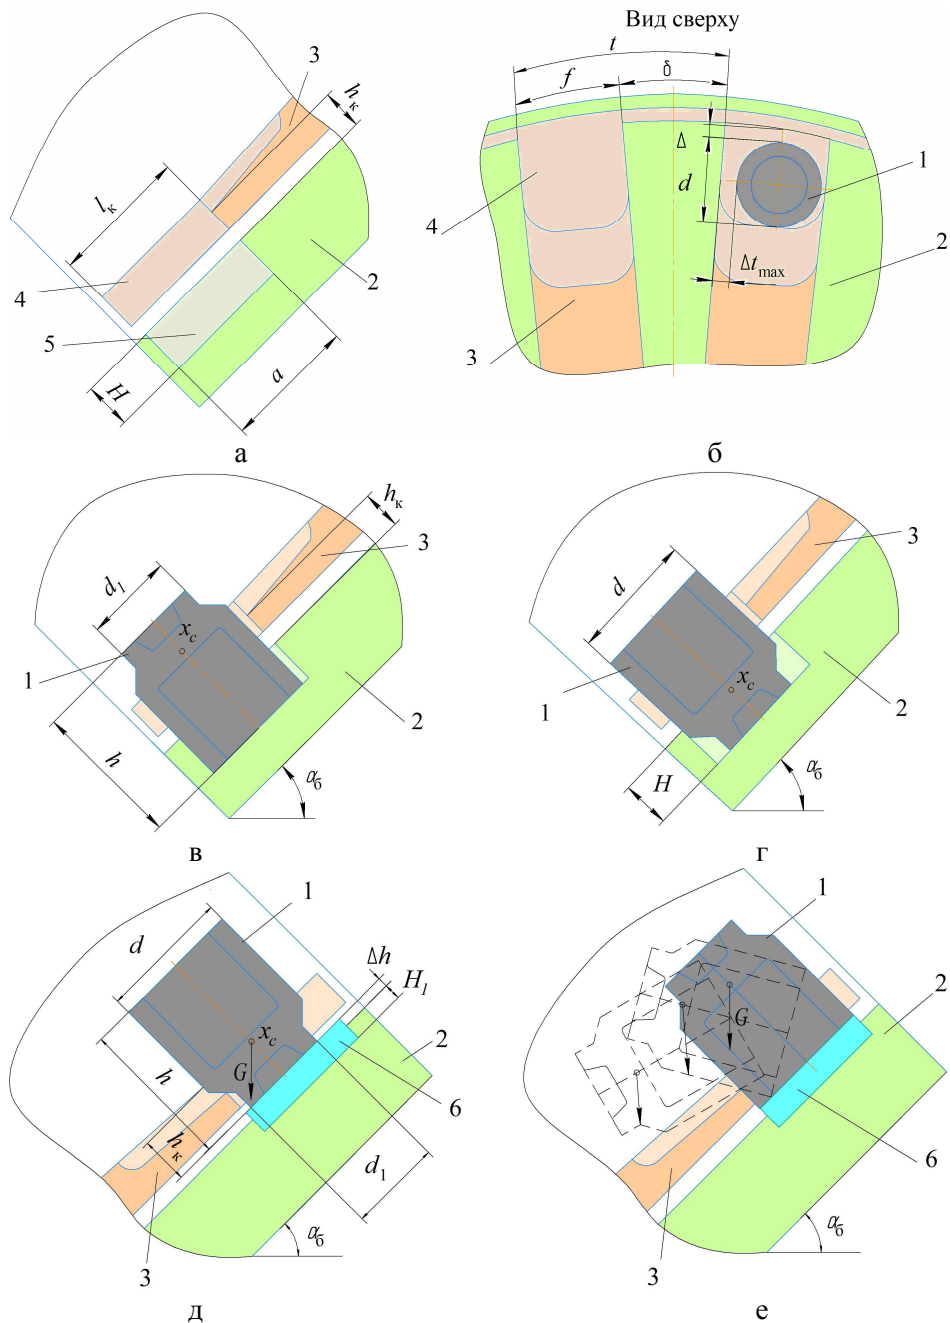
Схемы совершенствованного бункерного загрузочного устройства для деталей, близких к равноразмерным с асимметрией по торцам: а – общий вид; б – вид сверху; в, г – в нижней части бункера БЗУ с запавшей в разных положениях деталью; д, е – в верхней части бункера БЗУ с запавшей деталью: 1 – деталь; 2 – основание; 3 – диск; 4 – карман; 5 – кольцевой паз; 6 – копир
